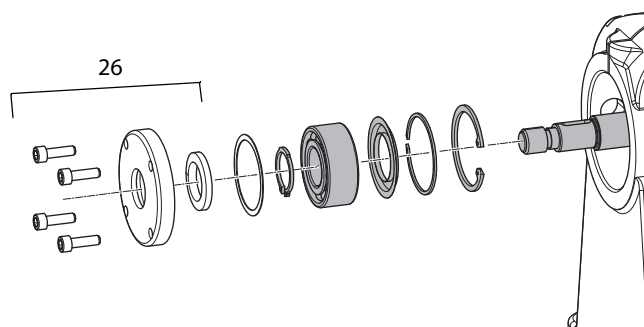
Forma constructiva L1, eje de la bomba, lado de la bomba
